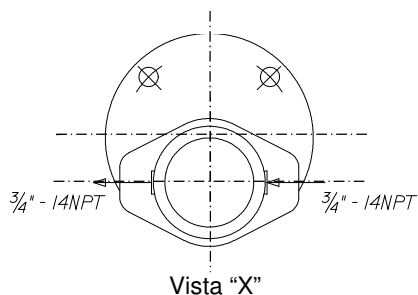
Bomba de engranaje instalada en el eje de la bomba
